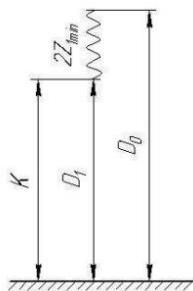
Размерные цепи при обработке наружной поверхности Ø22h11
